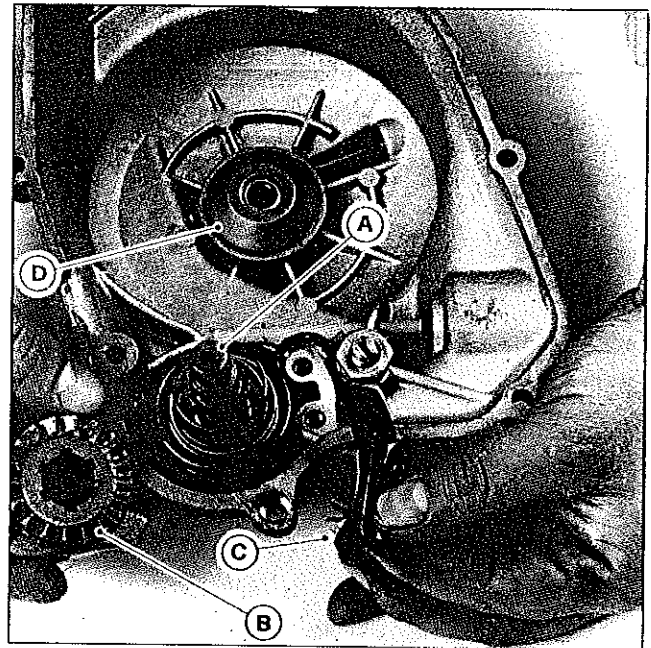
A. EIXO PEDAL DE ARRANQUE
